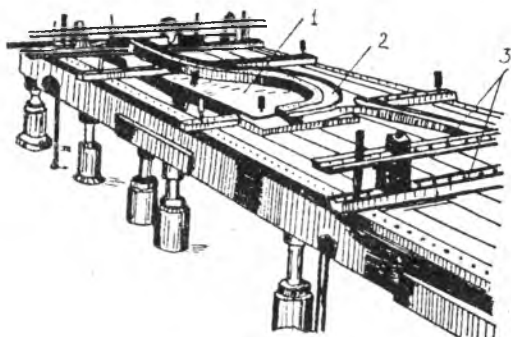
Установка шаблона и рубильника на плаз-кондукторе: 1—шаблон контура агрегата в определенном сечении; 2—рубильник, фиксирующий контур агрегата в этом сечении; 3—поперечные линейки
